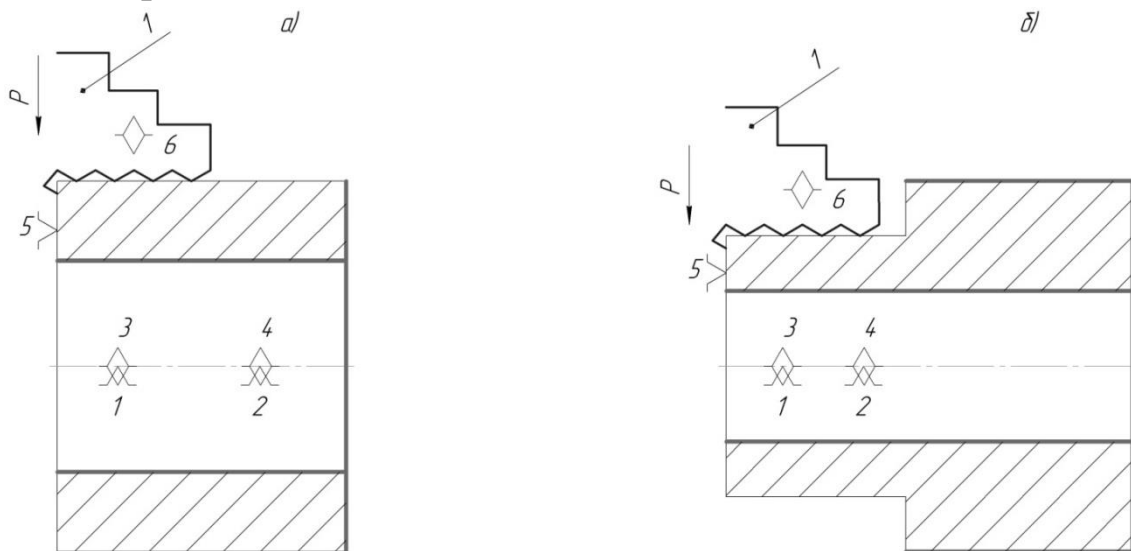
Схемы базирования при выполнении 1-ой операции обработки зубчатых колес: а – без ступицы; б - со ступицей
